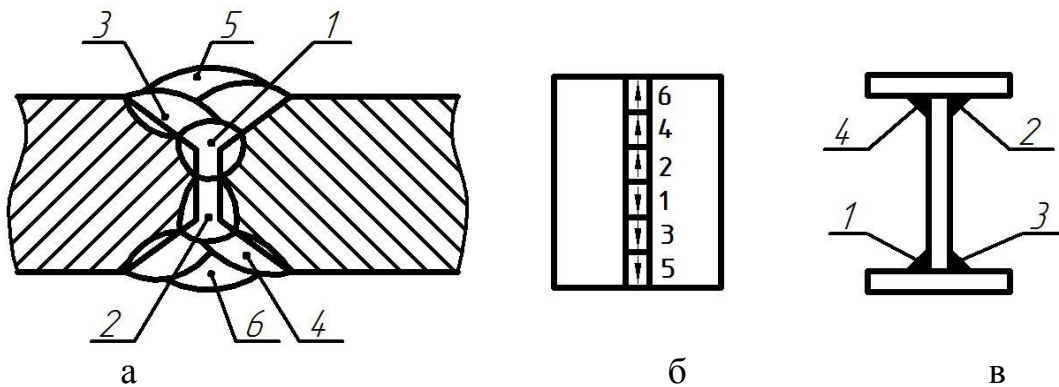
Раціональна послідовність (1, 2, ...) накладання зварних швів: а – при багатопрохідному зварюванні у межах поперечного перерізу; б – при зварюванні довгих швів; в – при зварюванні просторових конструкцій
